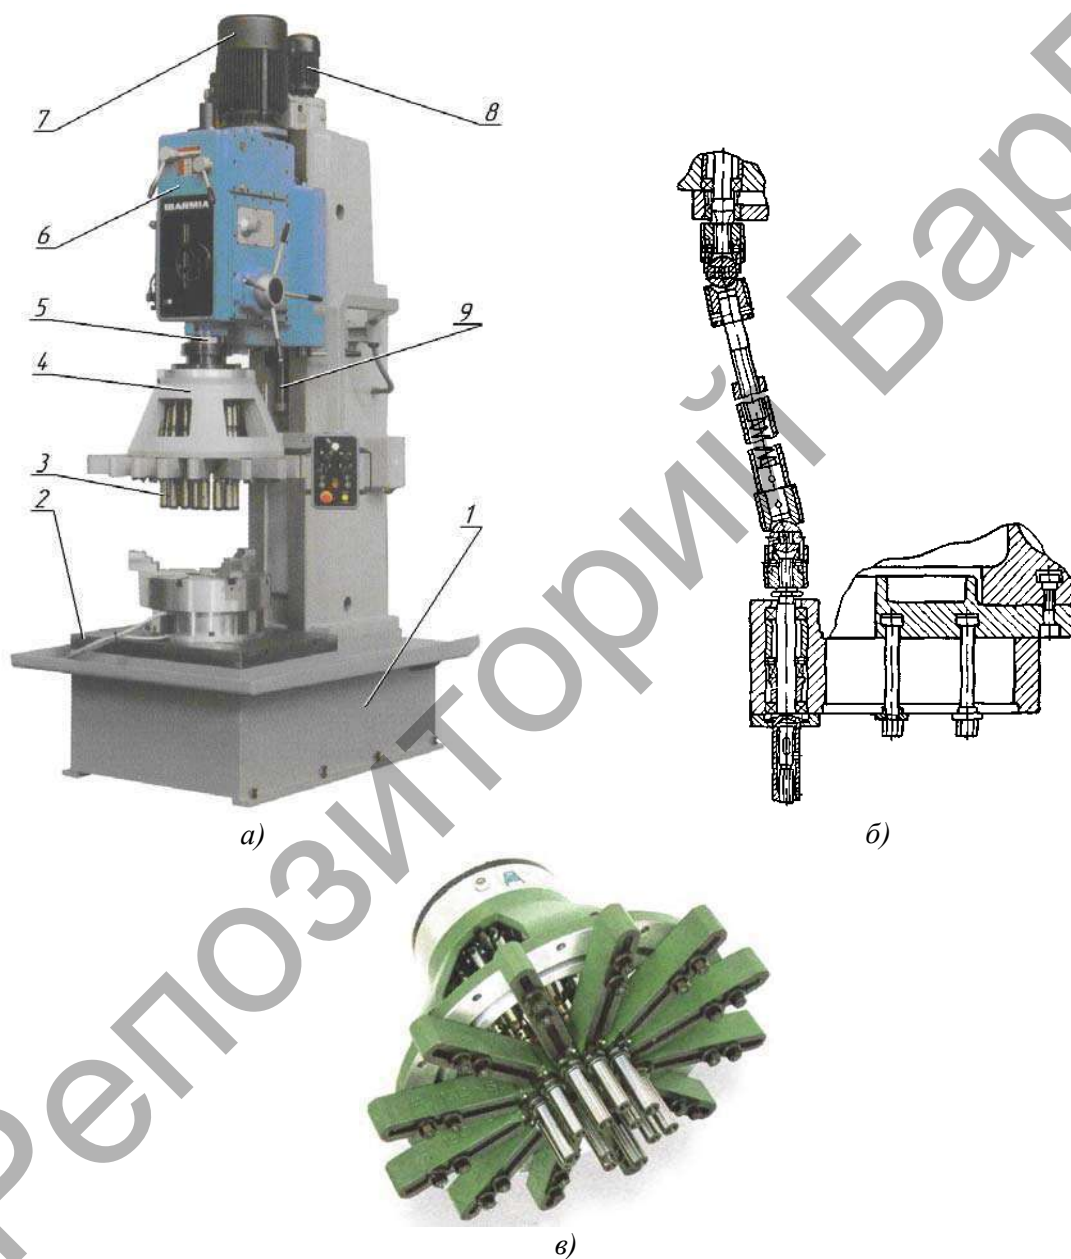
Многошпиндельный сверлильный станок с постоянными шпинделями
